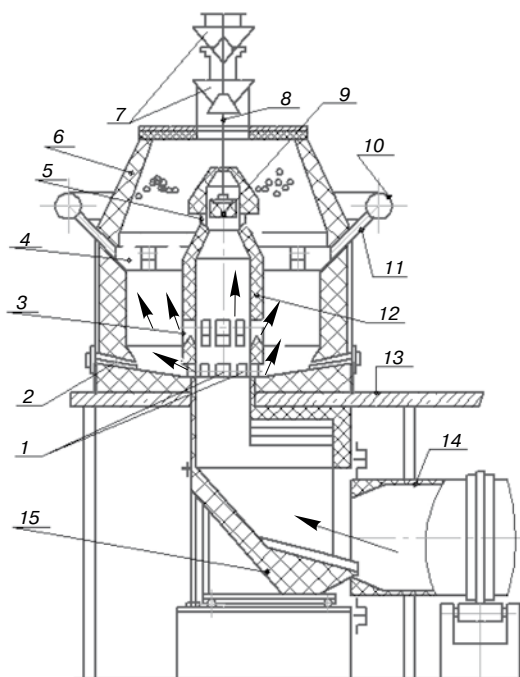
Шахтный противоточно-прямоточный подогреватель-декарбонизатор сырья
